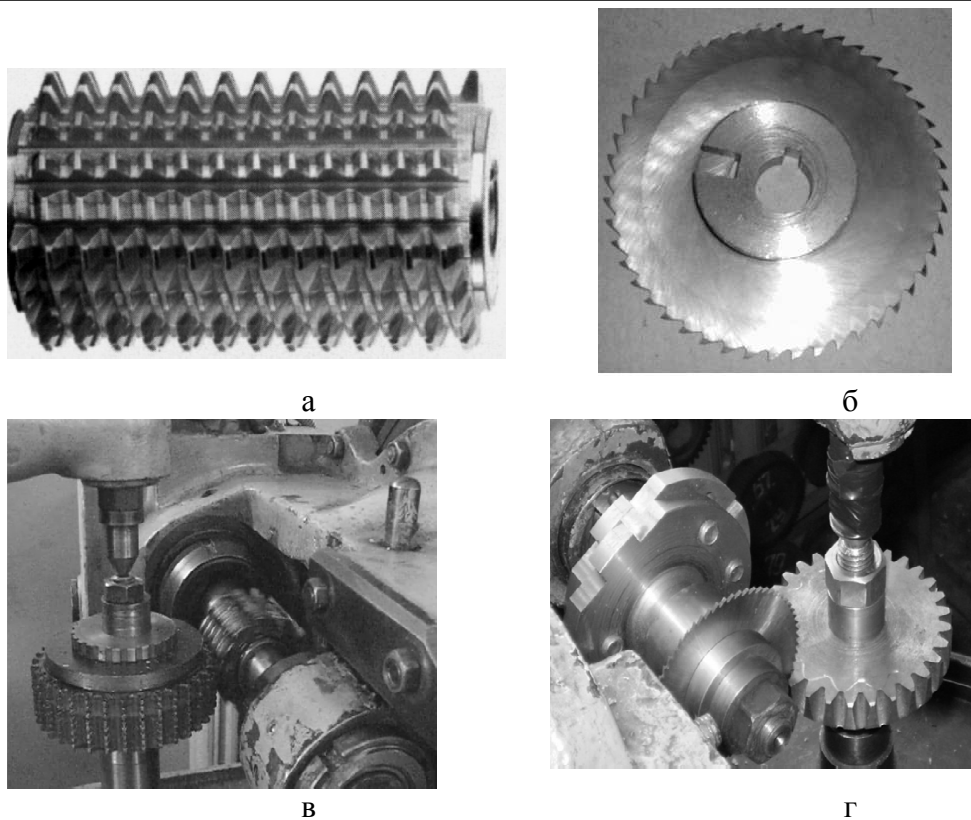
Черв'ячна фреза (а) і дискова фреза з ексцентричною оправкою (б) та робоча зона зубофрезерного верстат при зубонарізанні черв'ячною (в) і дисковою (г) фрезами
